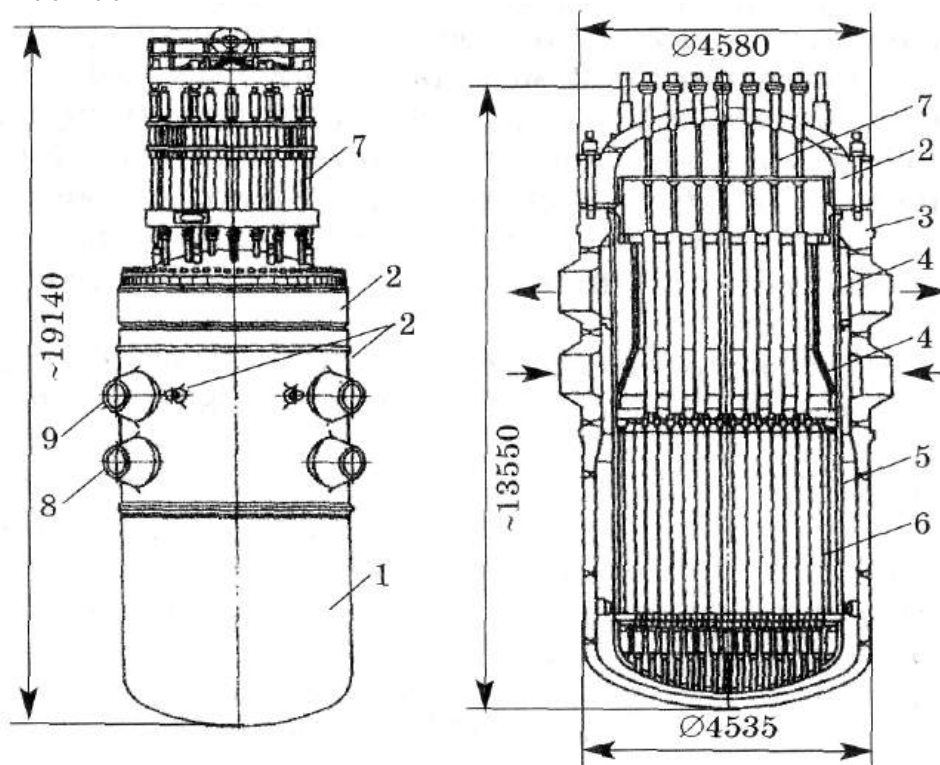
Загальний вигляд реактора ВВЕР-1000: 1 - корпус реактора; 2 - кришка реактора; 3 - внутрішньокорпусна шахта; 4 - блок захисних труб; 5 - загородження активної зони; 6 - активна зона; 7 - механізми управління СУЗ; 8 - вхідний патрубков; 9 - вихідний патрубков; 10 - патрубки підключення системи аварійного охолодження активної зони
